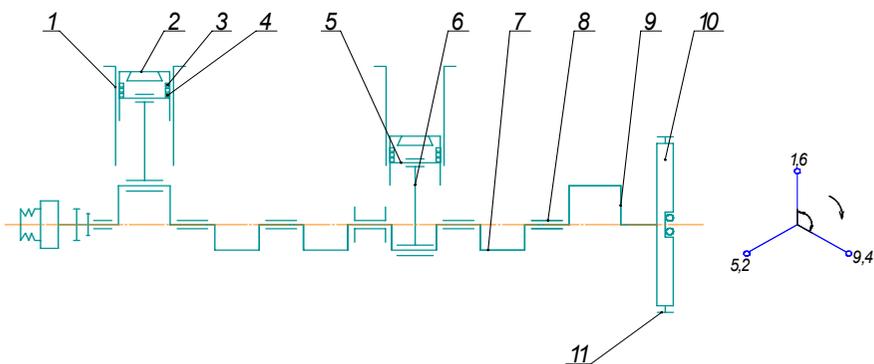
Схема кривошипно-шатунного механизма двигателя Д-260:
